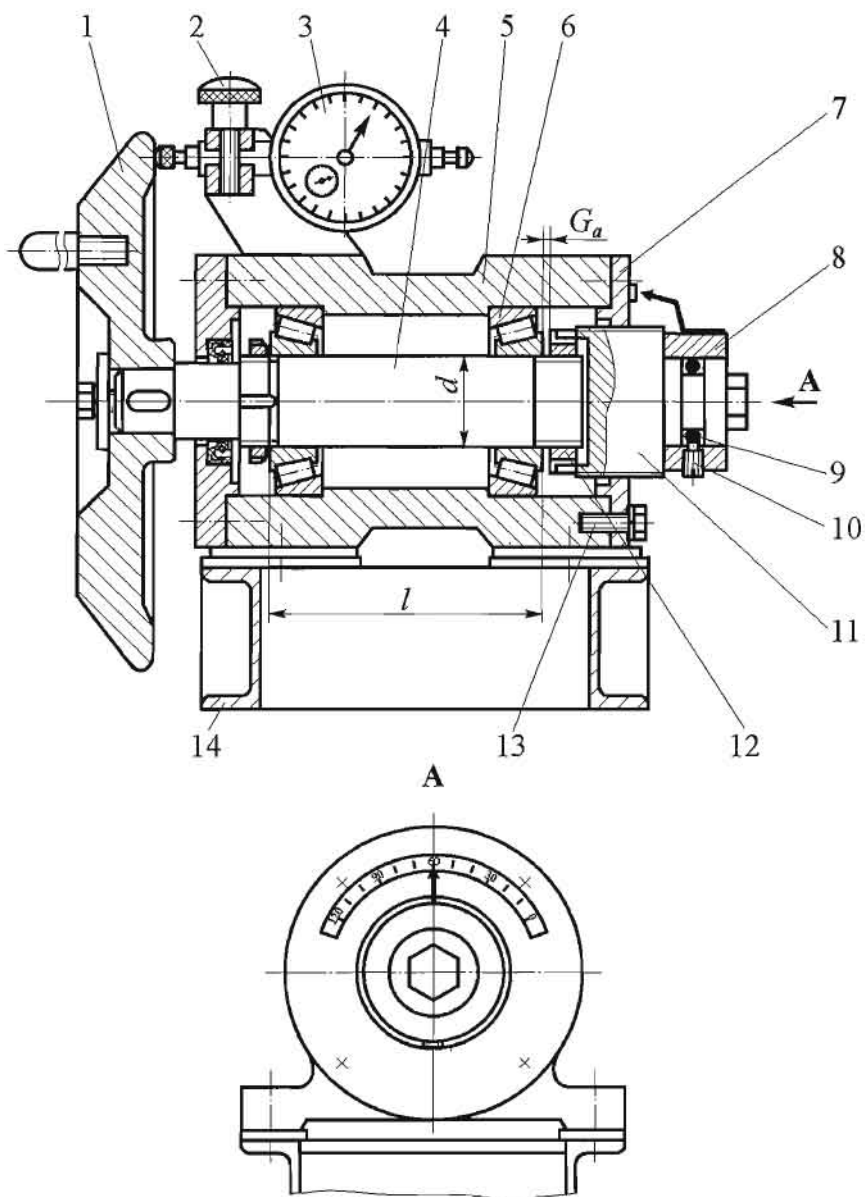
Конструкция лабораторной установки при установке подшипников по схеме III
